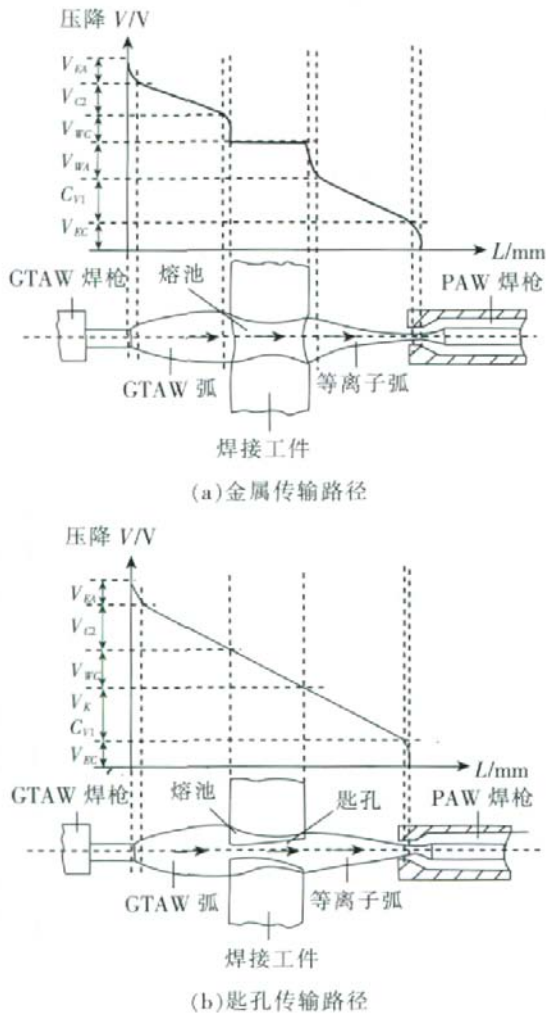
双面 PAW+GTAW 工艺焊接电流传输路径
